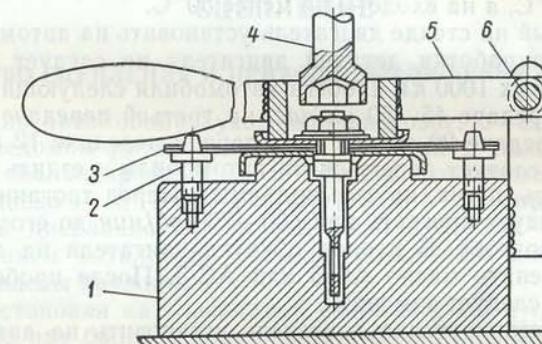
Приспособление для сборки диафрагмы топливного насоса:
